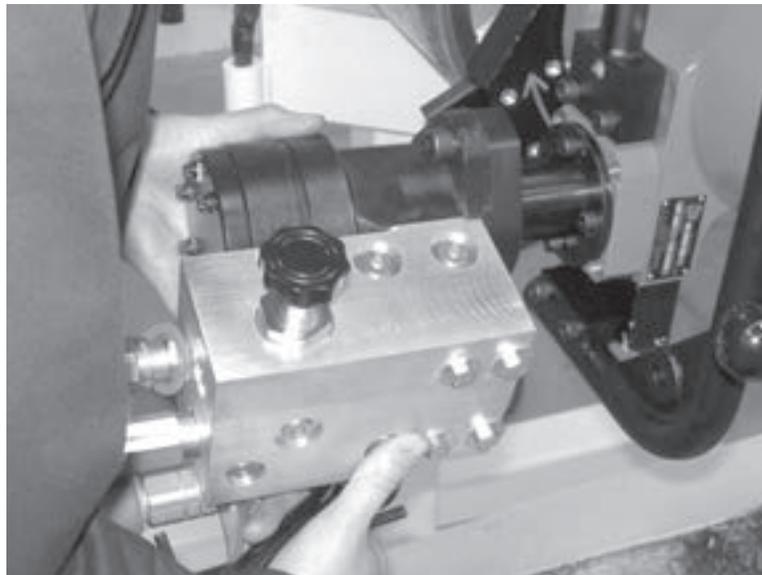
El motor hidráulico es intercambiable con el motor neumático.
